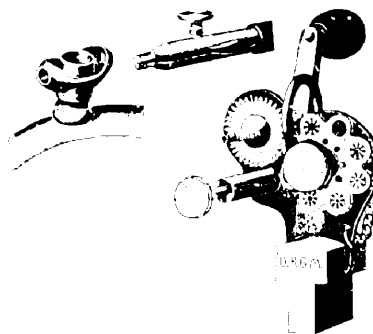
Bügel-Fräsapparat und Pendantloch-Fräser
